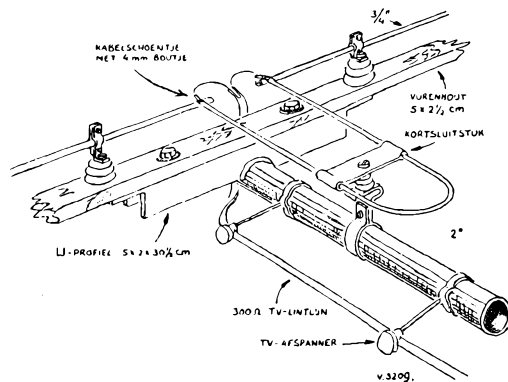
Detailtekening van de constructie zoals die door PAoCT werd toegepast
